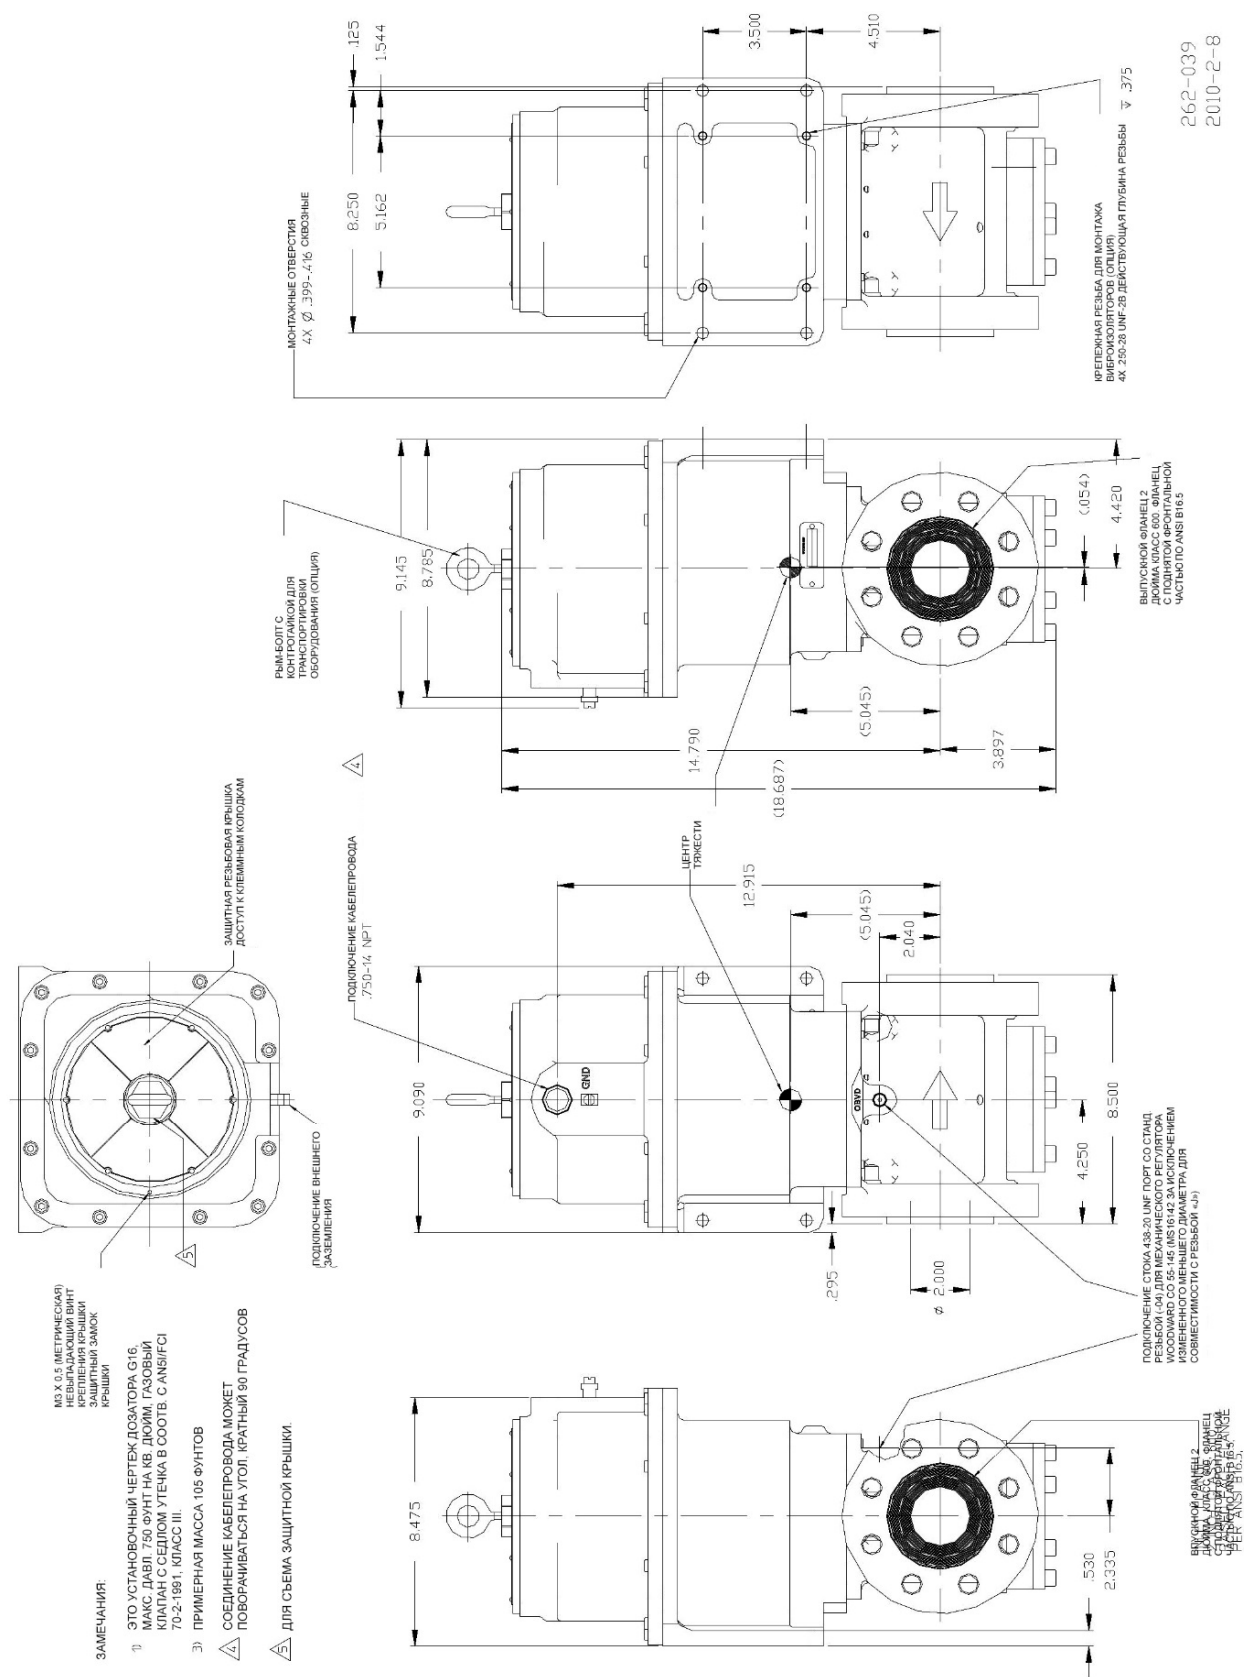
Габаритный чертеж дозатора GS16 (стандартный дозатор, один кабелепровод)
